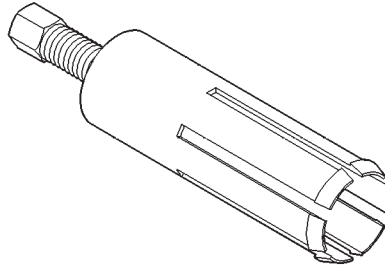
Dichtung in hinteren Lagerhalter einbauen
